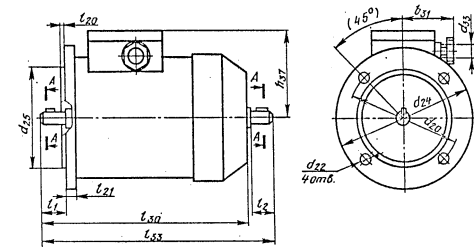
Габаритные, установочные и присоединительные размеры двигателей исполнений 1М3081, 1М3082
